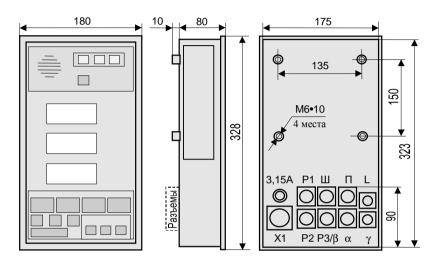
Габаритные и присоединительные размеры БОДа
